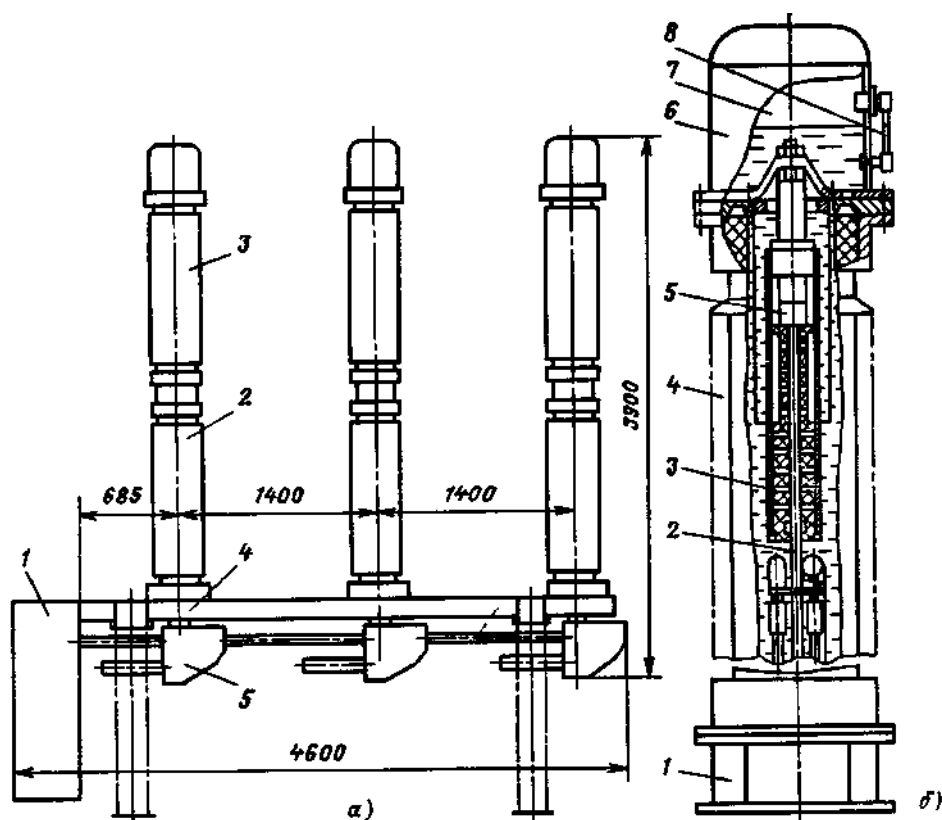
Малообъемный масляный выключатель типа ВМТ-110Б: а) – общий вид; б) – дугогасительный модуль; 1 – привод ППК-2300; 2 – изолятор опорный; 3 – дугогасительное устройство; 4 – вывод; 5 – рама
